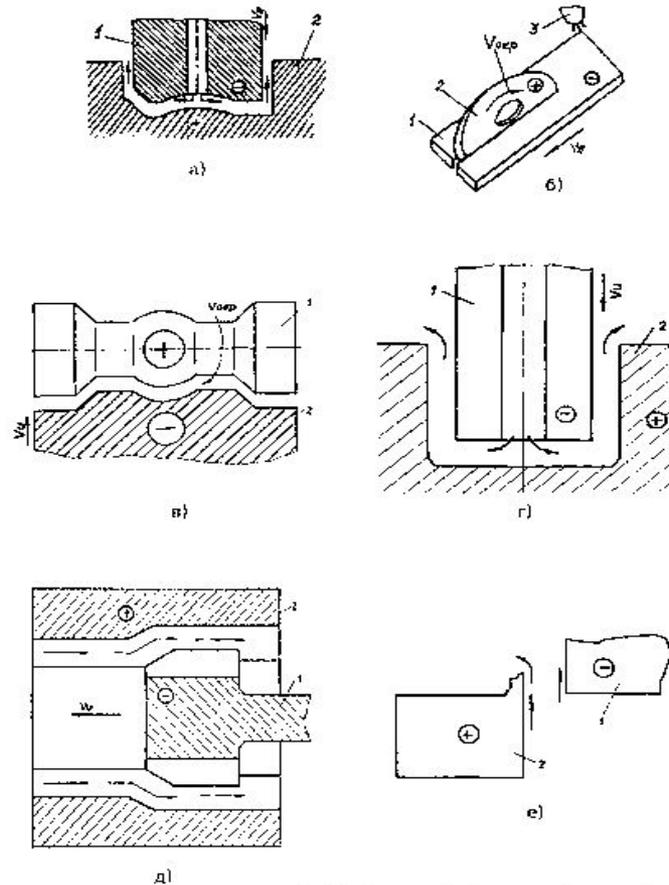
Схема электрохимической обработки: а) объемное формообразование. 1 - электрод-инструмент; 2 - заготовка; б) отрезка: 1 - заготовка; 2 - диск; 3 - сопло; в) точение: 1 - заготовка; 2 - ЭИ; г) шлифование: 1 - ЭИ; 2 - заготовка; д) калибрование: 1 - ЭИ; 2 - заготовка; е) удаление заусенцев: 1 - ЭИ; 2 - заготовка
